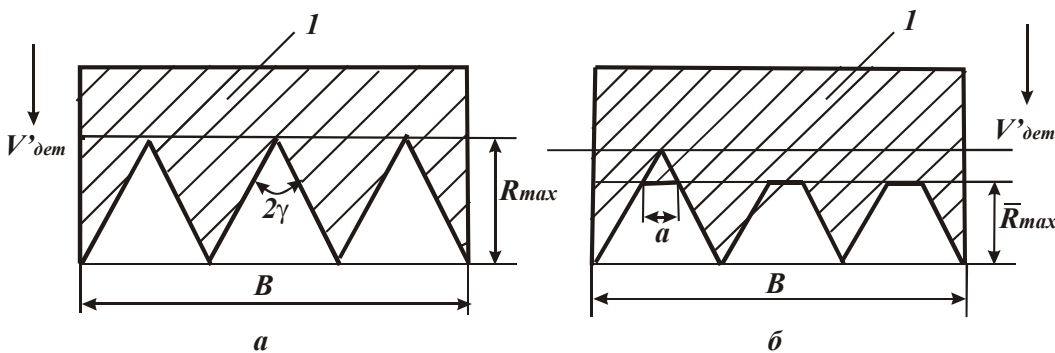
Розрахункові схеми формування шорсткості поверхні при обробці гострими (а) та притупленими (б) зернами.
